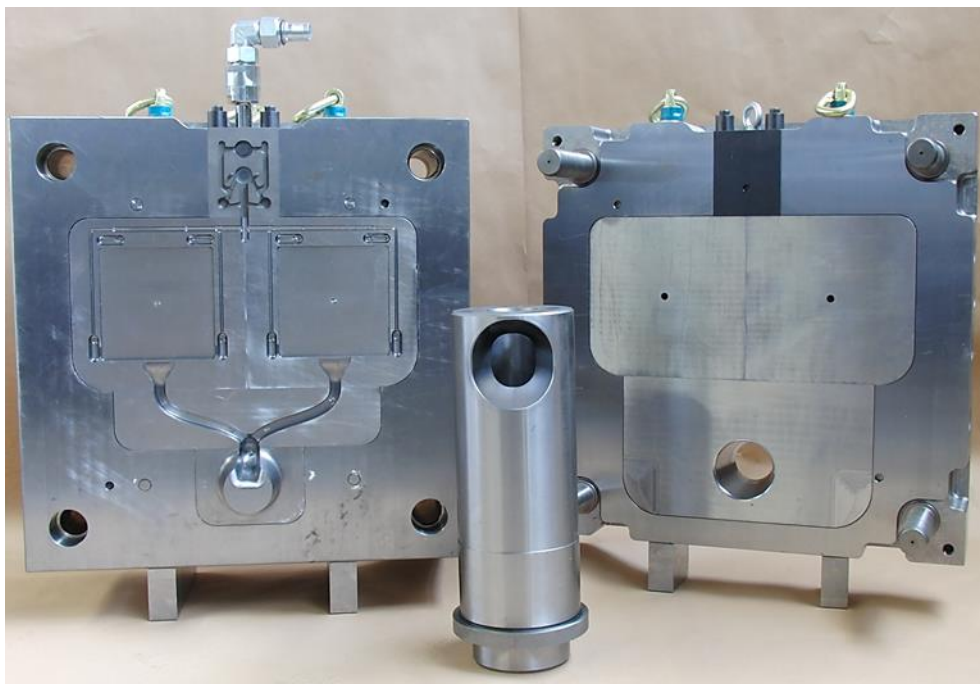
Versuchswerkzeug Zwillingsplatte mit Gießkammer (Innendurchmesser 60 mm) und modularen Einsätzen inklusive zwei Kavitäten.
